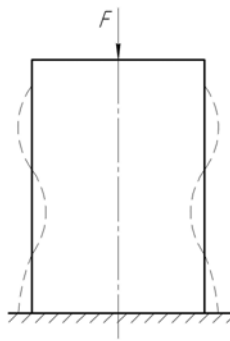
Появление гофров при осевом сжатии цилиндрической заготовки
